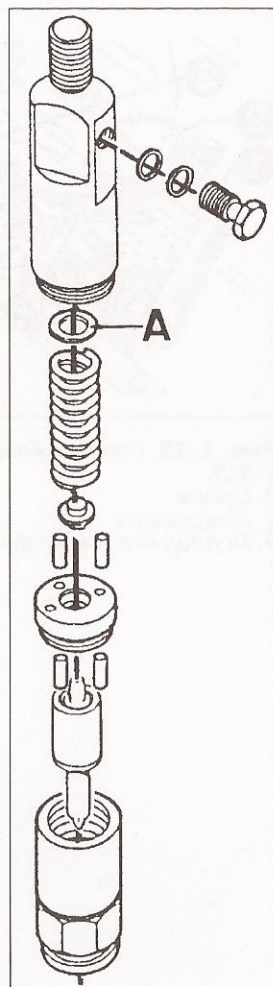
Корпус форсунки и форсунка (4-цилиндровый и 6-цилиндровый двигателя)
